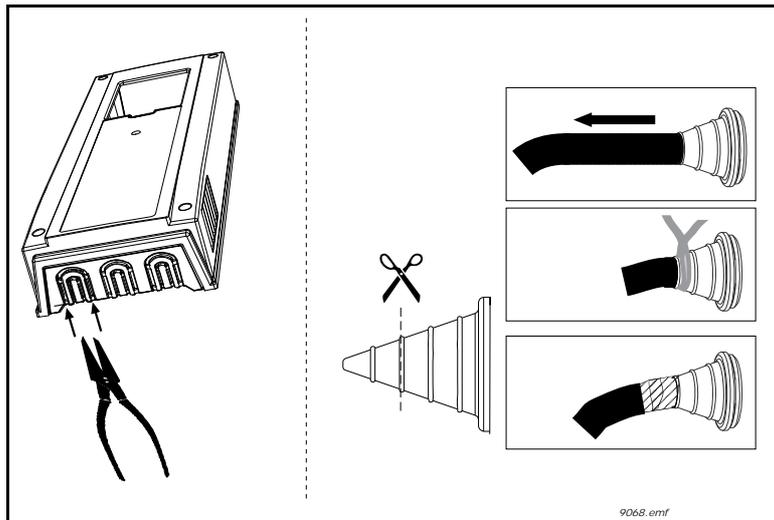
Kabeldurchführung. Links: IP21, rechts: IP54.
